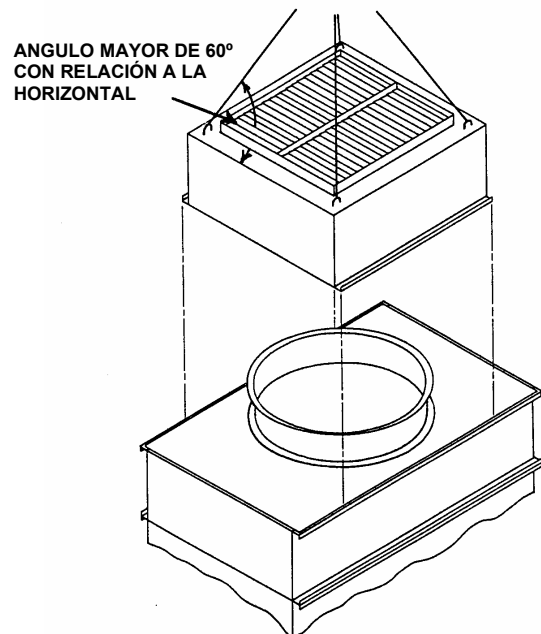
Acoplamiento de la Campana de Descarga con Compuerta a la Sección de Batería - Ventilador
